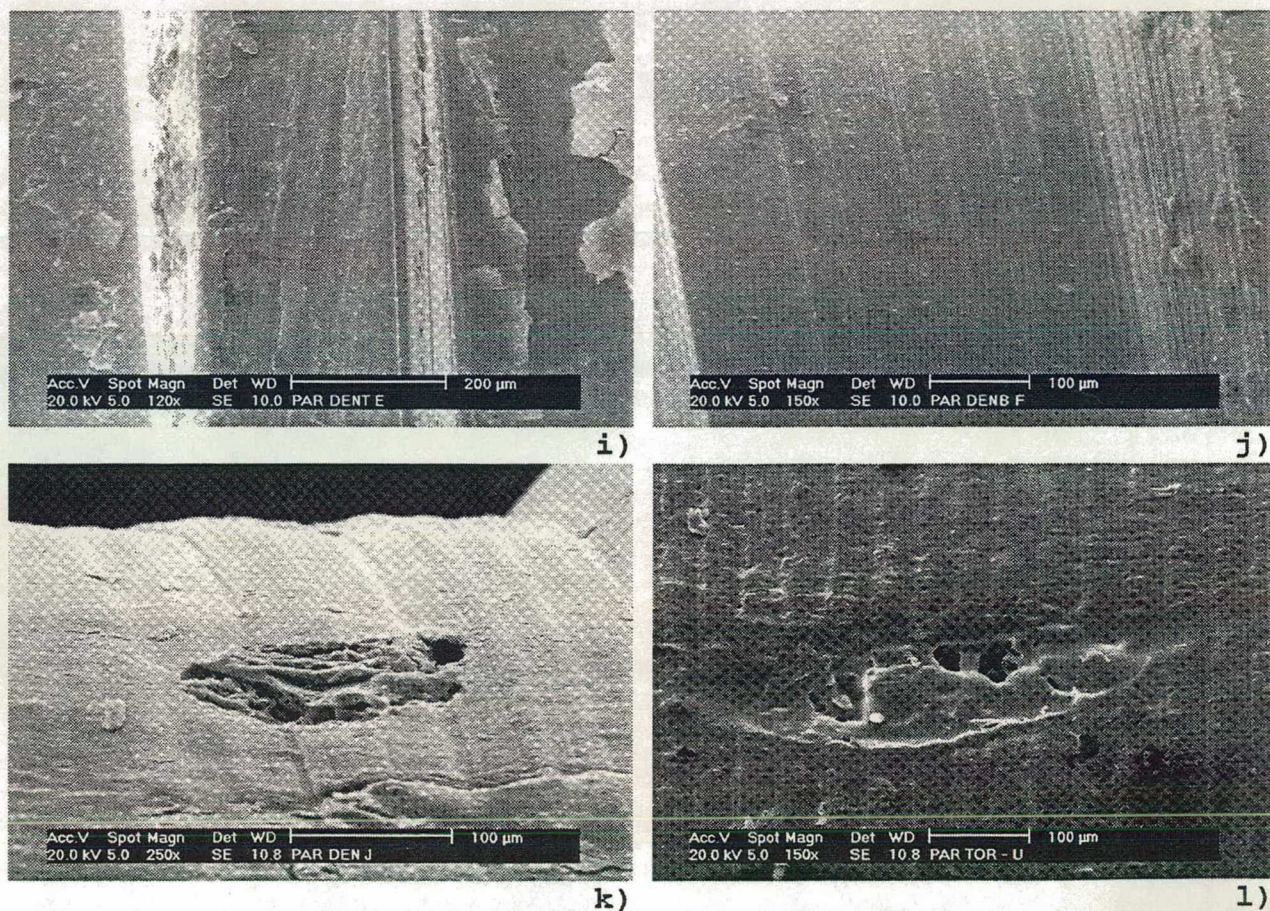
(Continuação) Ilustração de diferentes superfícies de implantes geradas por usinagem
